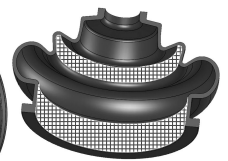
Section transversale (niveaux intermédiaire et inférieur)
